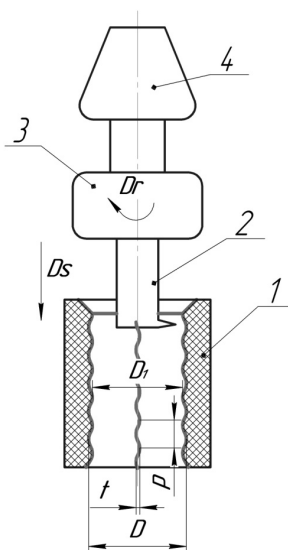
Схема фрезерування круглої різьби в АКМ
